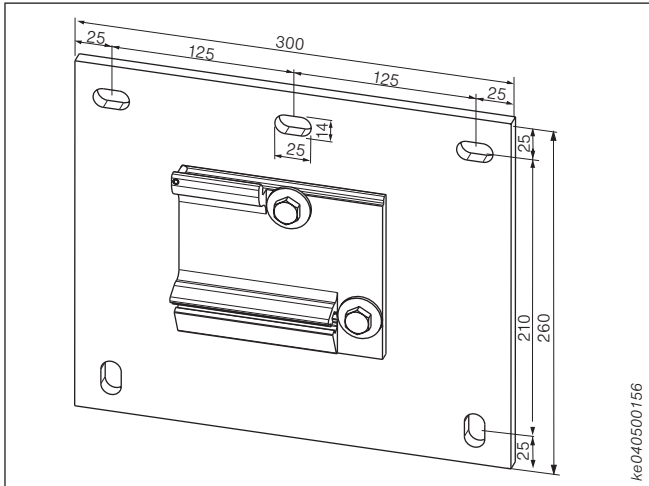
Consola tipo D – Fijación mural con placa de montaje
